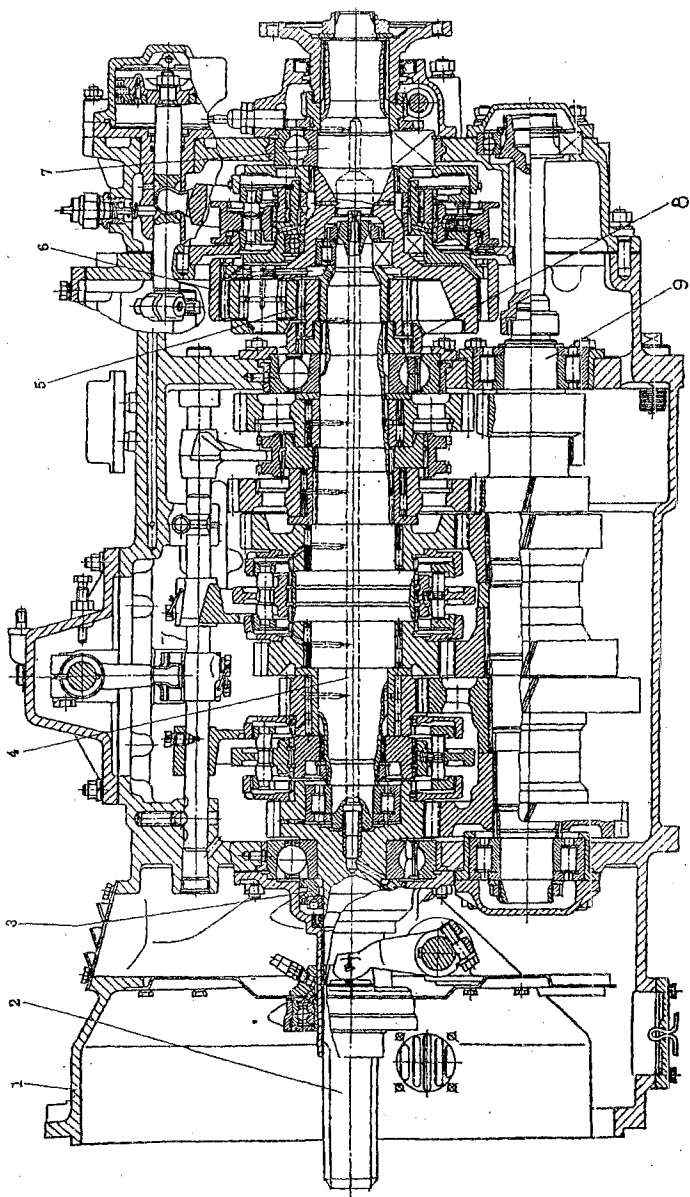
Чертеж девятиступенчатой коробки передач ЯМЗ-202
